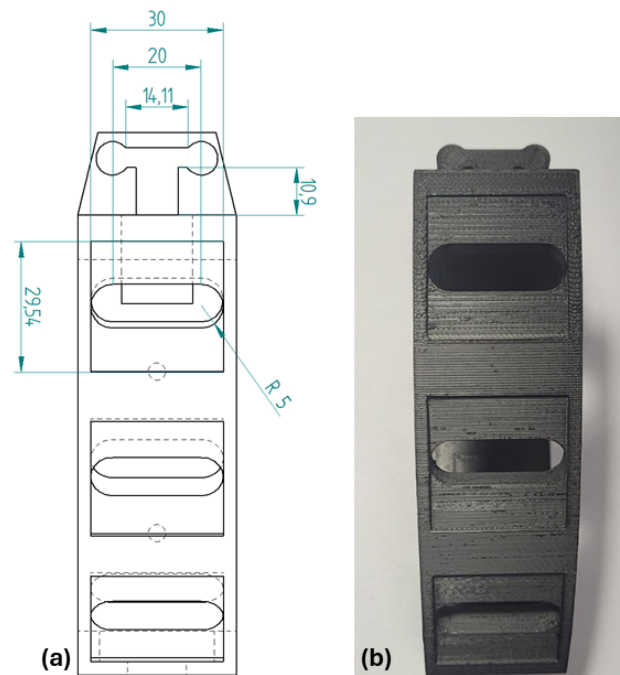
Vista superior do *rib*: (a) Desenho técnico (b) Peça impressa.
